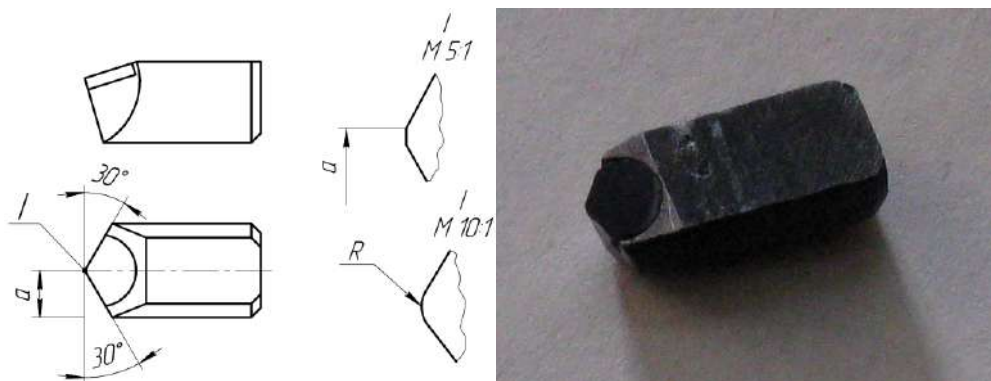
Конструкция и общий вид универсальной резцовой вставки с напаянной пластинкой СТМ «Белбор»
